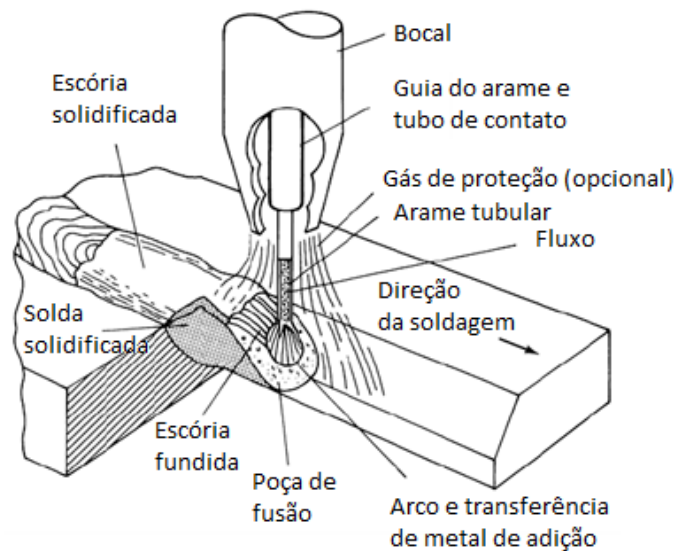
Processo de soldagem FCAW⁽¹⁴⁾.
